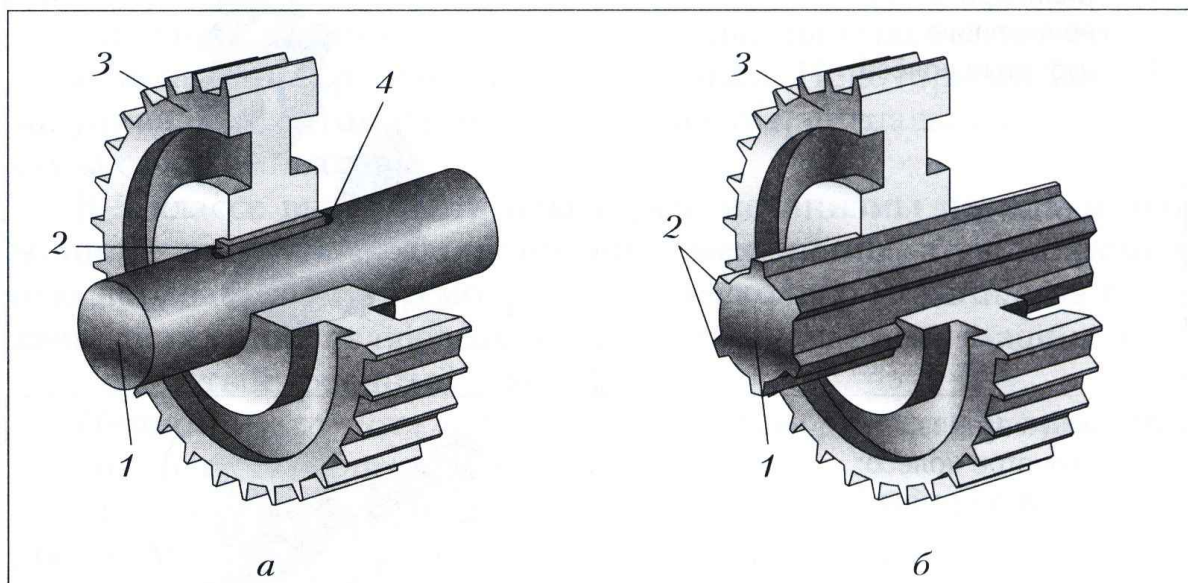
Соединение шестерни с валом: а — шпоночное: 1 — вал; 2 — шпонка; 3 — шестерня; 4 — шпоночный паз; б — шлицевое: 1 — шлицевой вал; 2 — шлицы; 3 — шестерня
